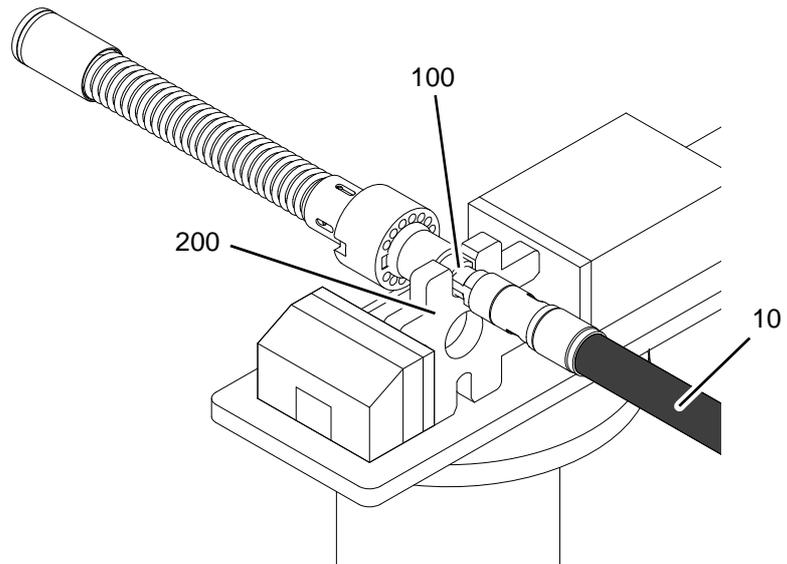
Desserrez le flexible de raccordement du tube de guidage
